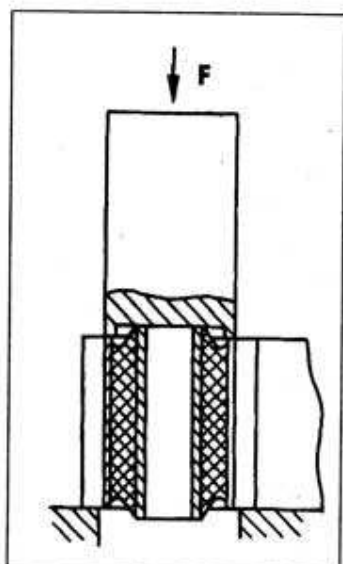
Выпрессовка шарнира из ушка рессоры
